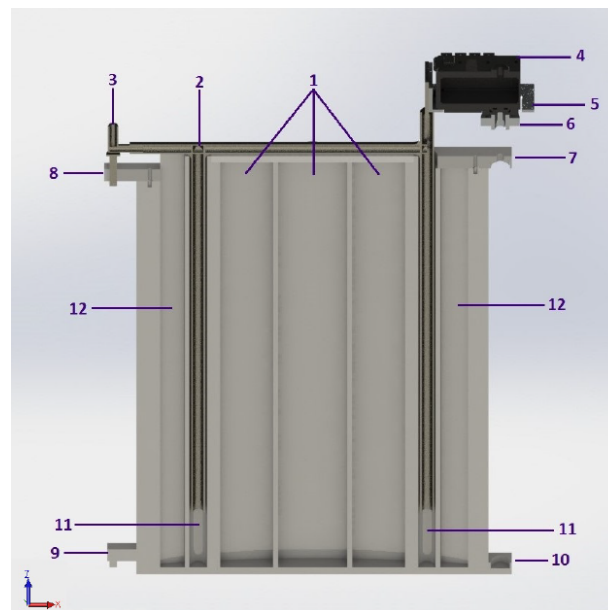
Coupe d'une section de la première version du robot. Le numéro 3 correspond à la pièce coudée s'encastant dans l'arbre de la section suivante.
